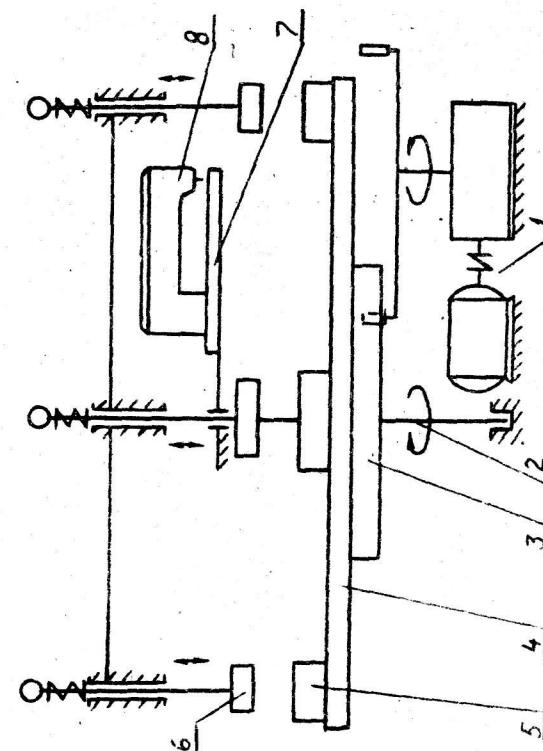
Кинематическая схема агрегата для сборки манжет мужской сорочки.
